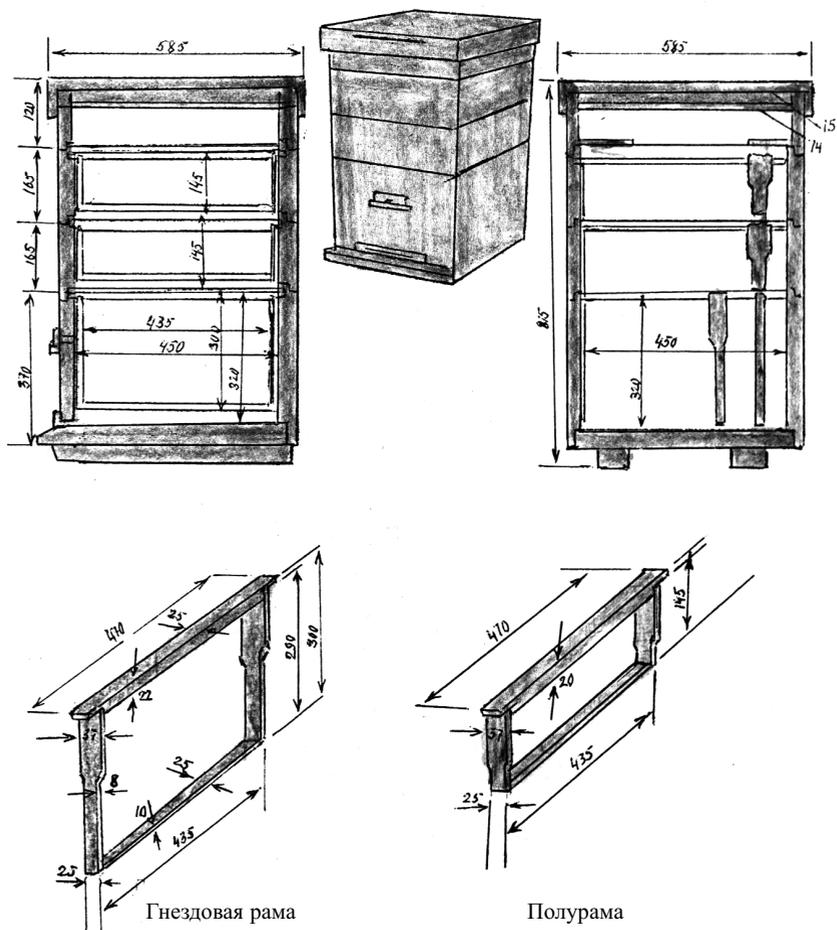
Однокорпусный улей с надставками, типовой проект 3.808.5-3
